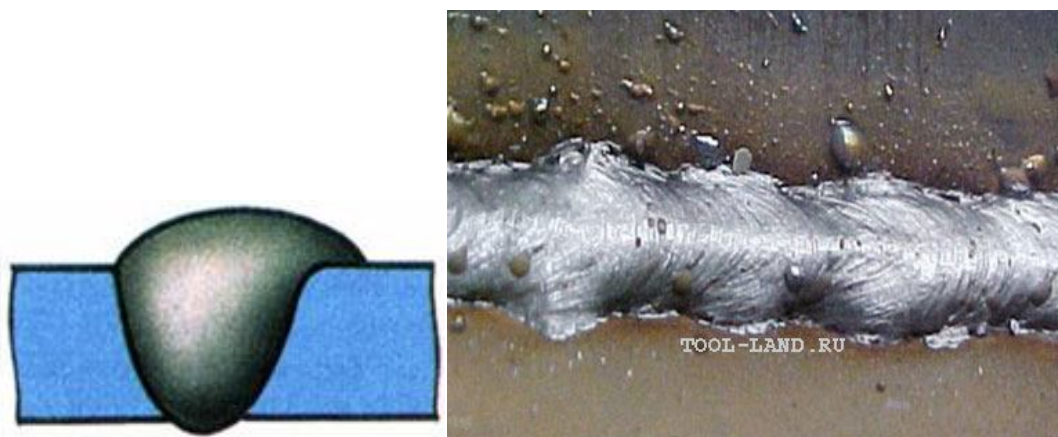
Дефекты сварного шва: наплывы
